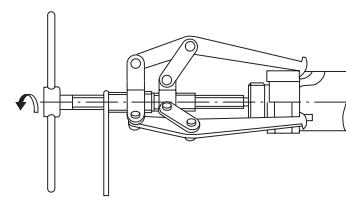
Demontage des Innenrings mit Abziehwerkzeug (2)
